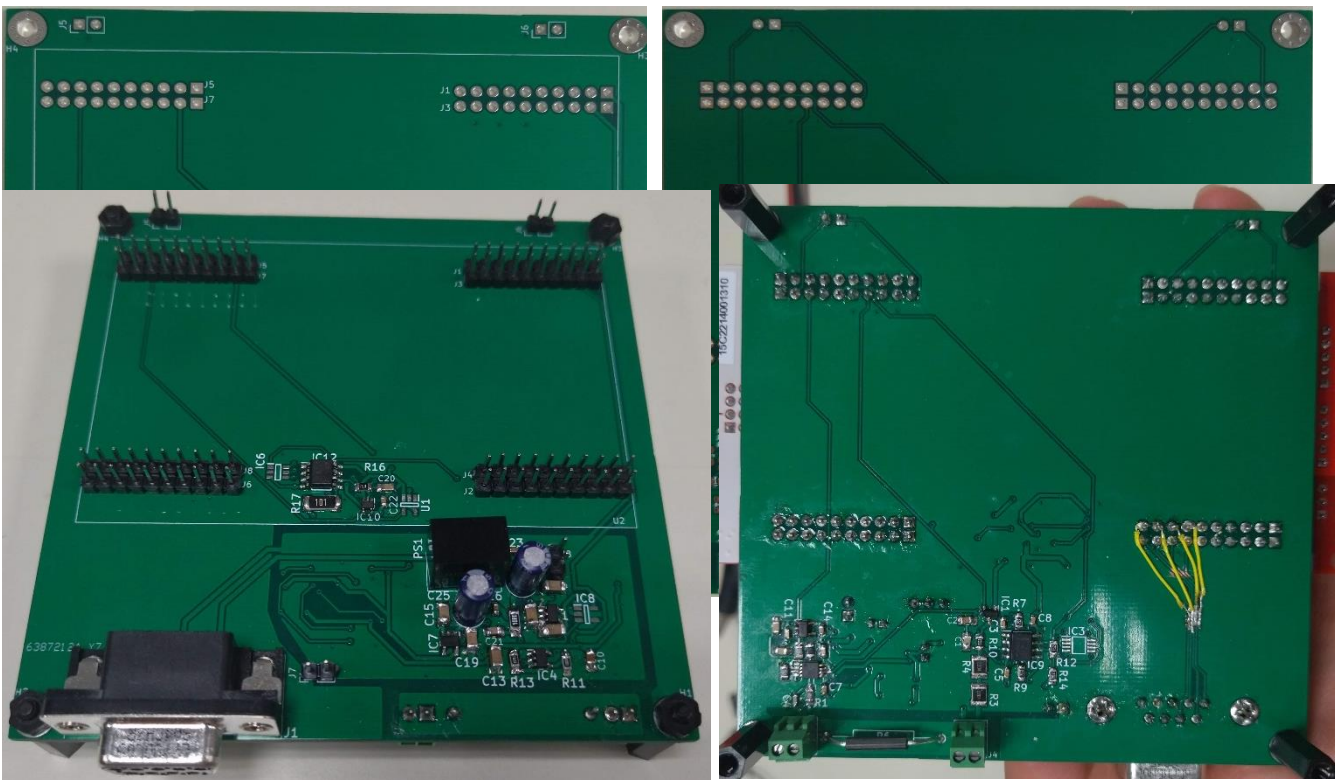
Lado Top y Bottom PCB de sensado soldada.
